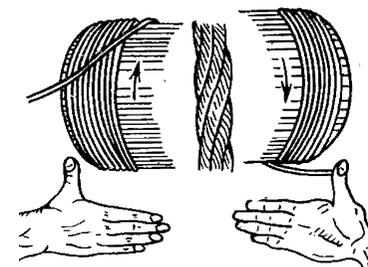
Определение направления однослойной навивки каната на барабан правой свивки
